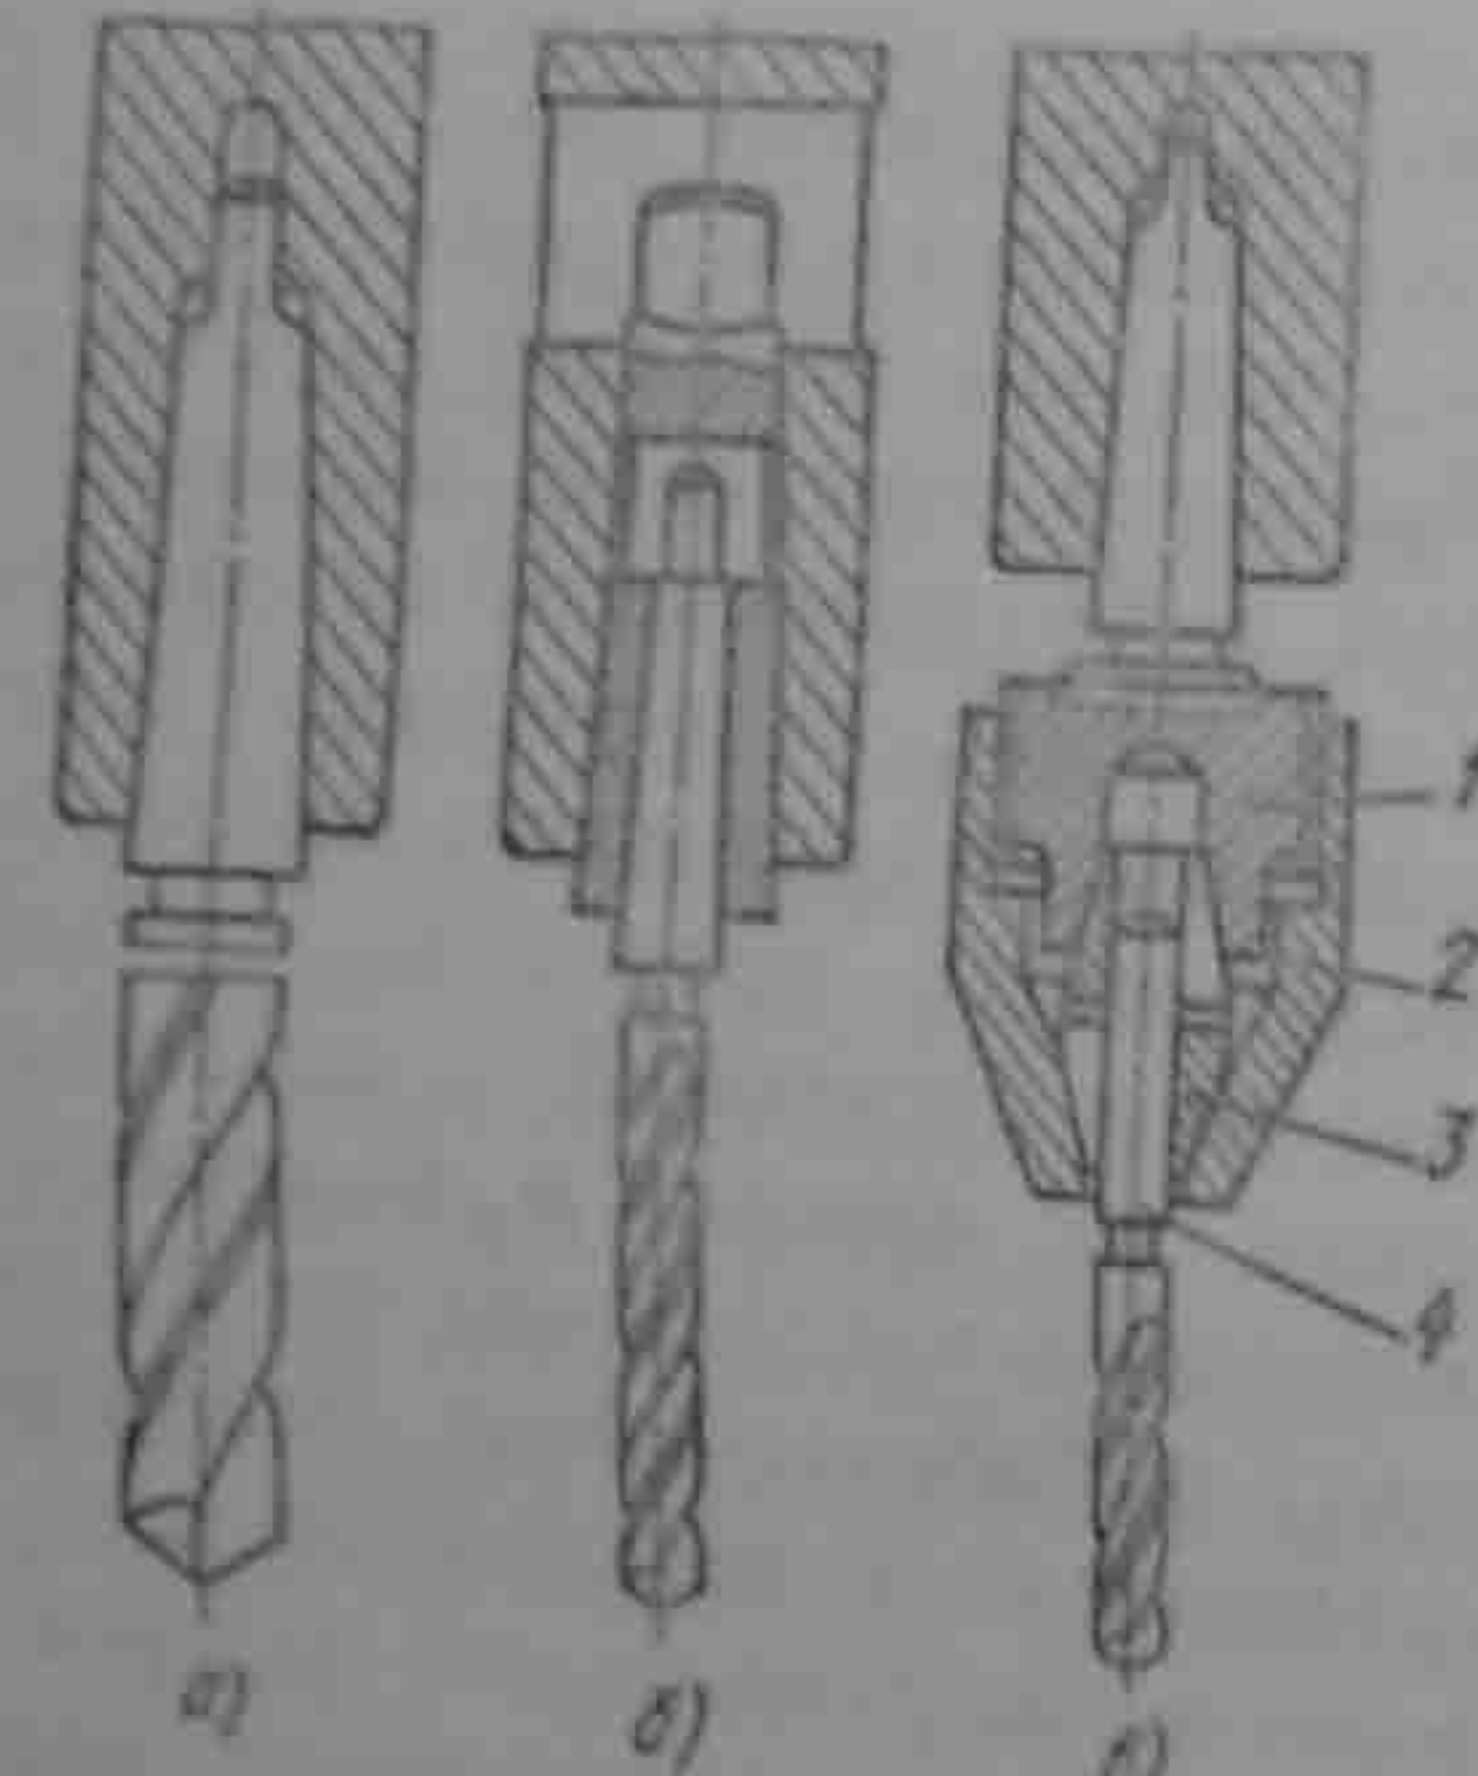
Схемы закрепления инструмента в шпинделе станка
